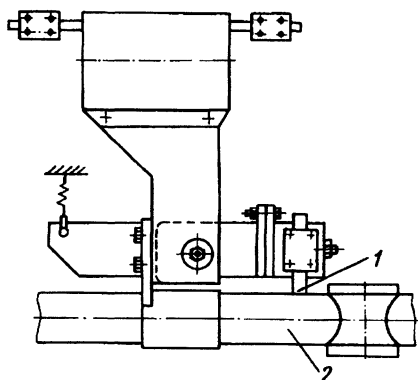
Устройство для контактного подвода тока (кондуктор) при непрерывной высокочастотной сварке
